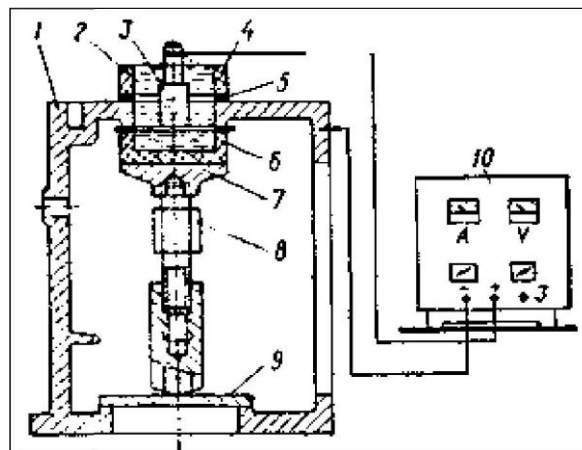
Установка місцевого електролітичного нарощування поверхні отвору в корпусній деталі:
